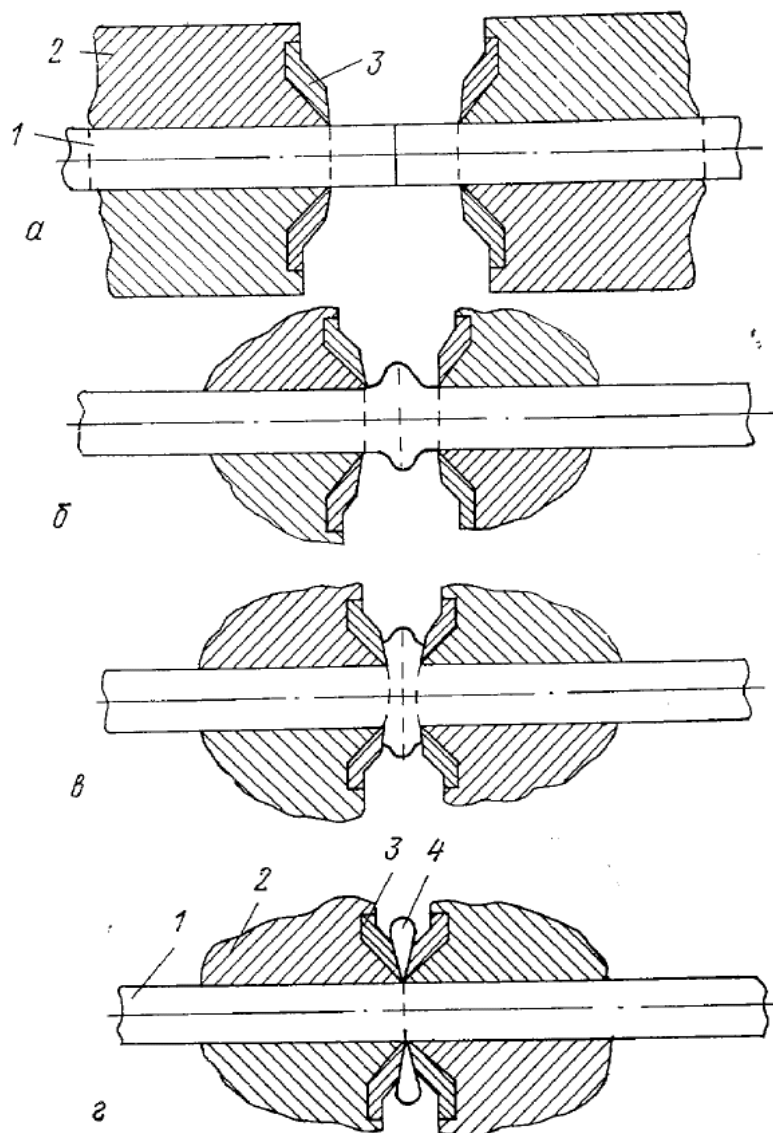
Сущность предлагаемого способа контактной стыковой сварки трубопроводов
